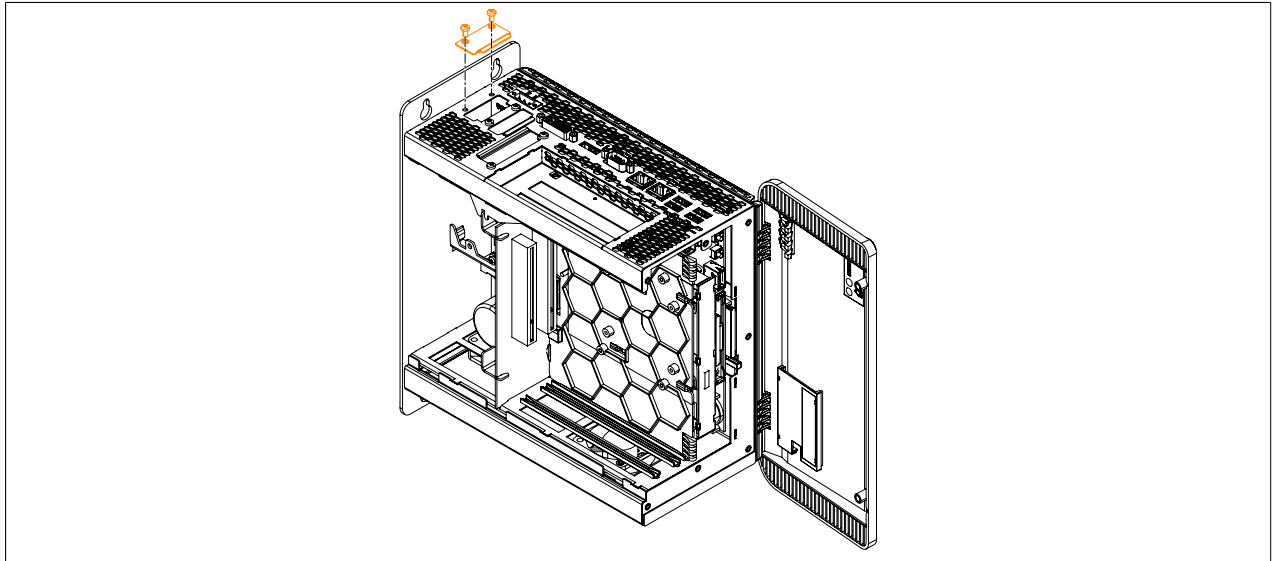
Torxschrauben und Blindabdeckung entfernen
